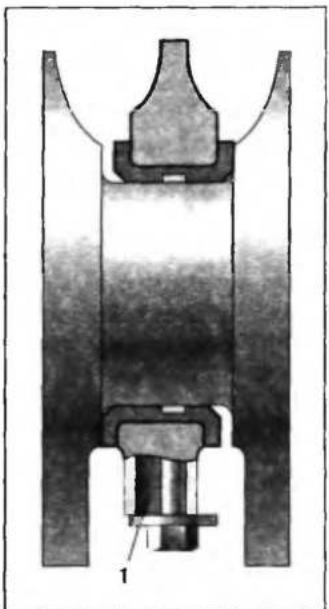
Схема уменьшения осевого зазора коленчатого вала сдвигом крышки упорного коренного подшипника в сторону хвостовика вала: 1 — отверстия в крышке под болты "разделаны" в сторону заднего фланца вала
